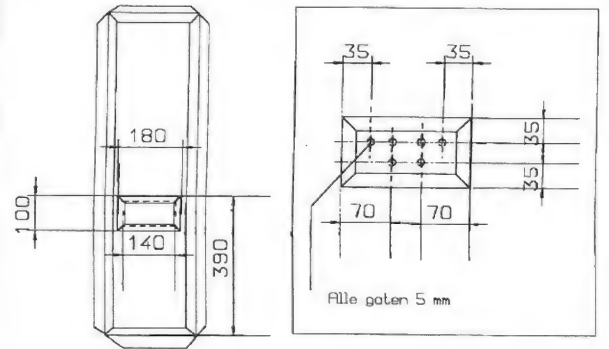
Zijaanzicht wooferbehuizing met buitenpanelen
